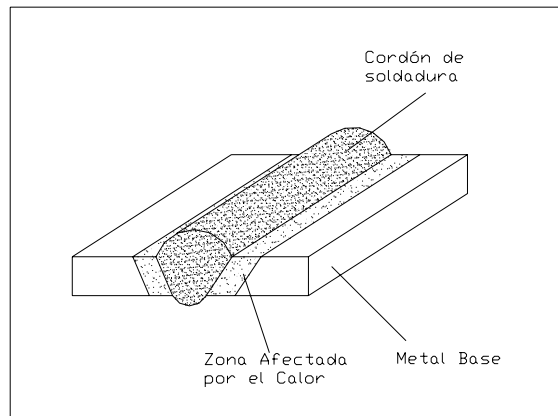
ZONAS DE LA SOLDADURA
